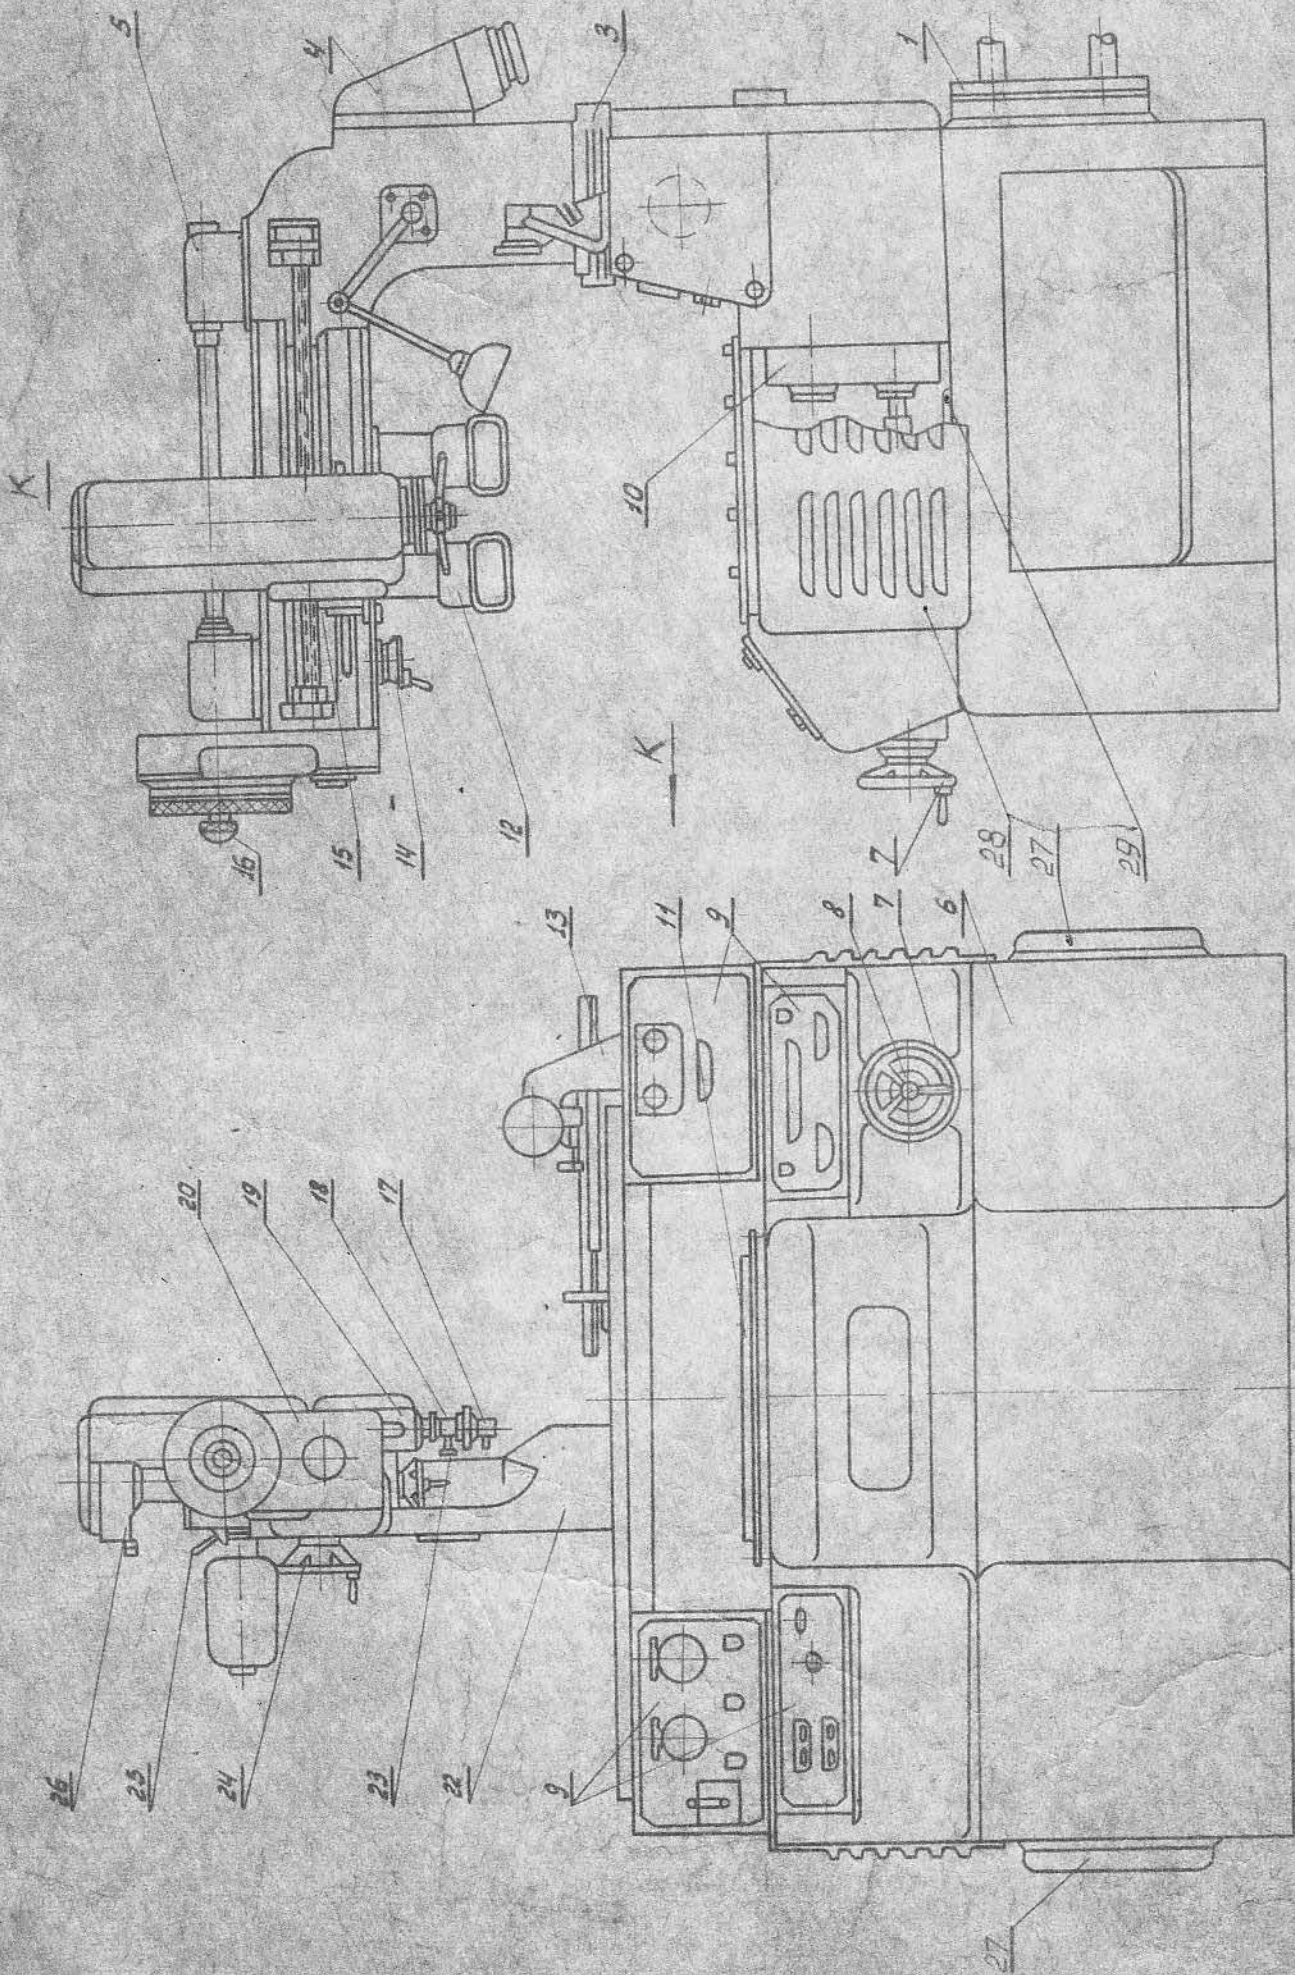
Общий вид станка с обозначением органов управления и основных узлов станка
